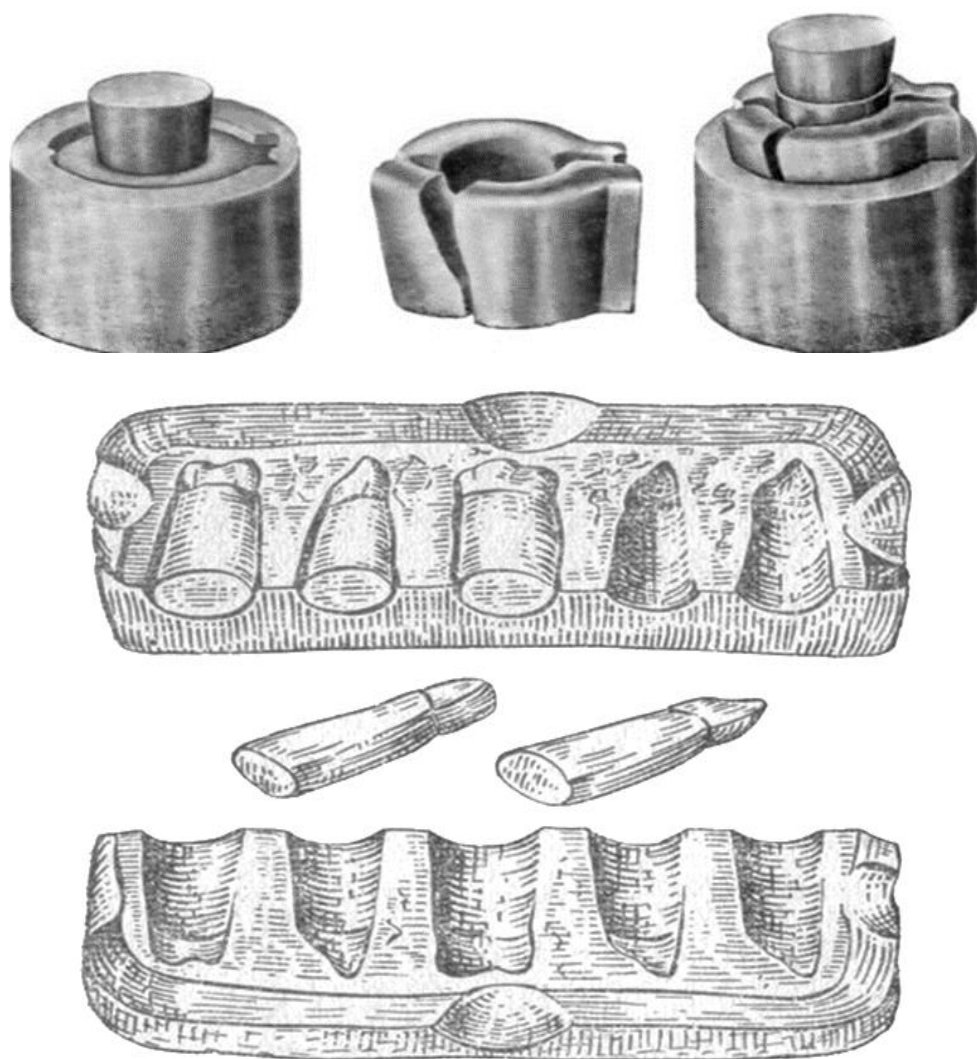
Виготовлення металевих штампів і металевої контрформи
